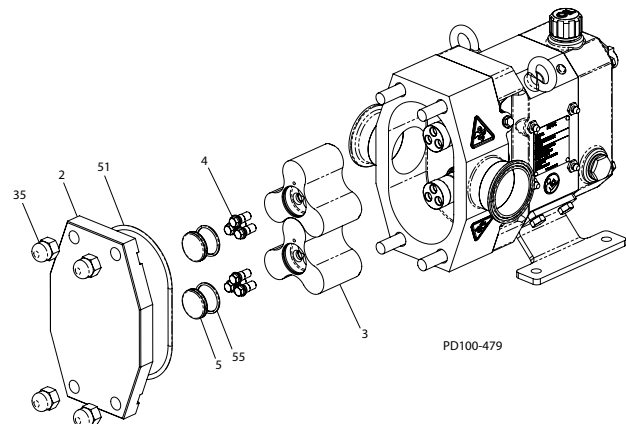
Desmontaje de la cubierta y del rotor de la bomba
